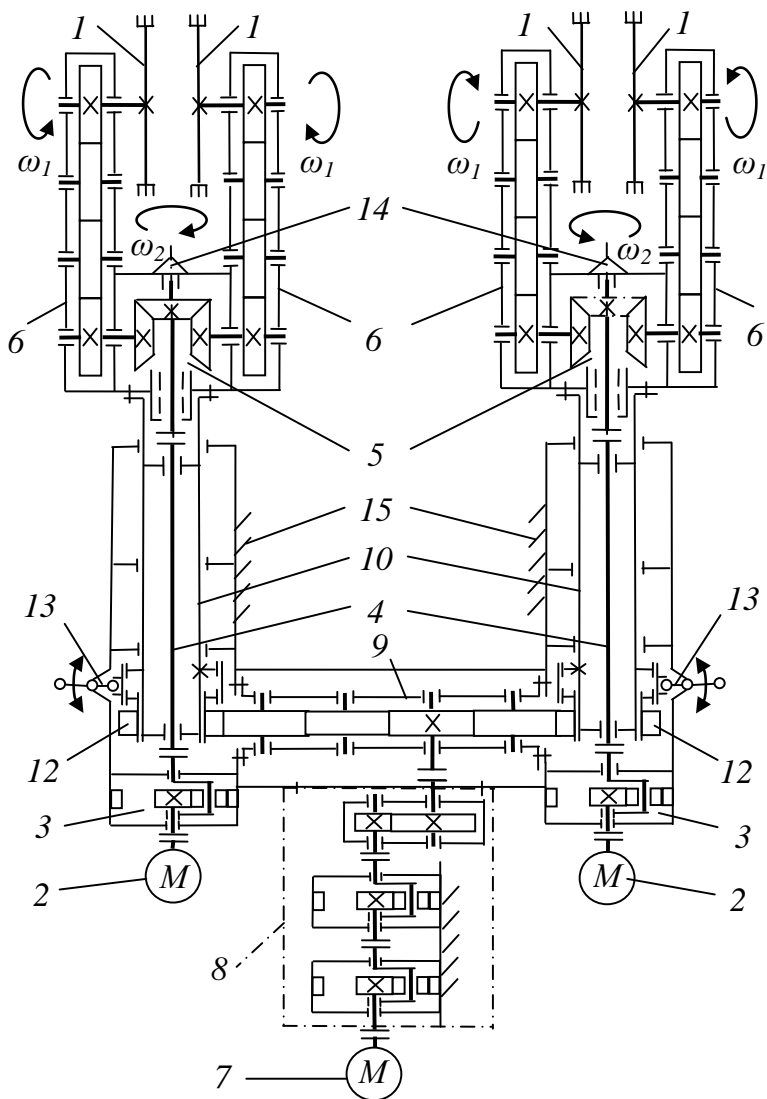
Кинематическая схема привода дисковых фрез
